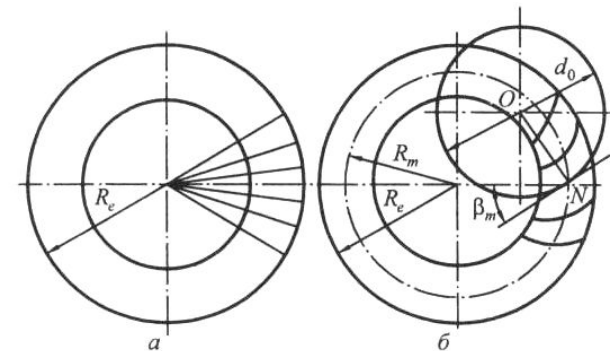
Форма линий зуба конического колеса: а — с прямыми зубьями; б — с круговыми зубьями
